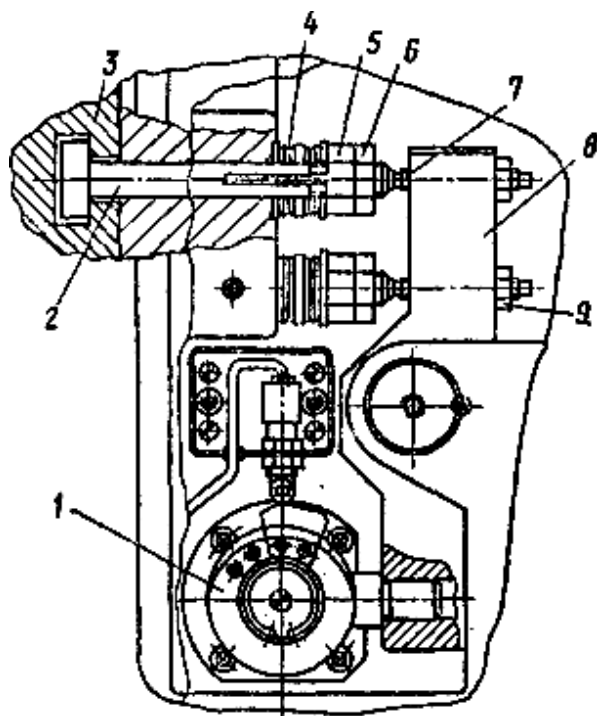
Механізм закріплення револьверної голівки на супорті верстата 2Р135Ф2–1
